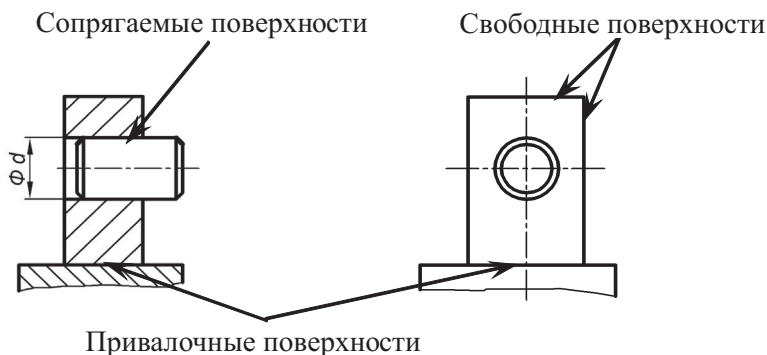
Поверхности сопрягаемые, привалочные, свободные
